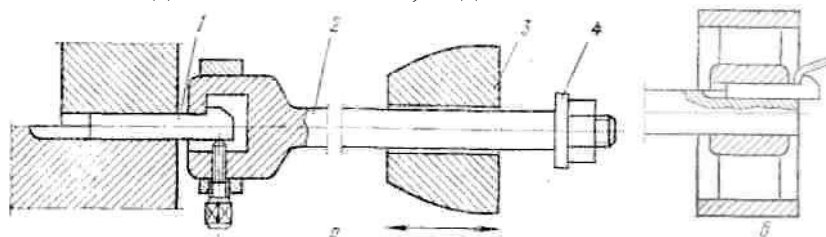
Приспособления для извлечения клиновидных шпонок с головкой
